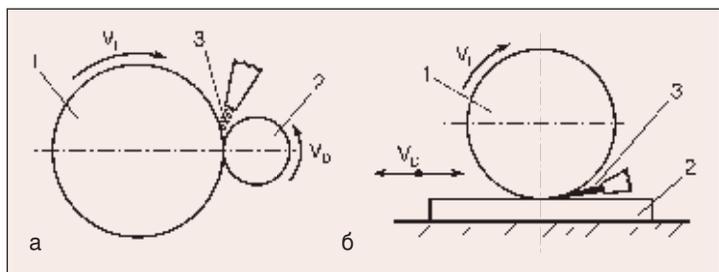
Схема механоімпульсної обробки циліндричних (а) і плоских (б) поверхонь: 1 — зміцнюючий інструмент; 2 — оброблювана деталь; 3 — технологічне середовище
